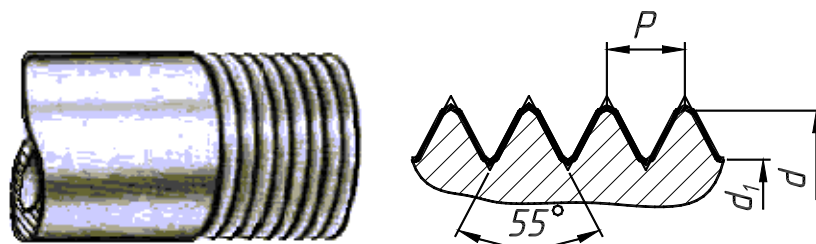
Профиль трубной цилиндрической резьбы
